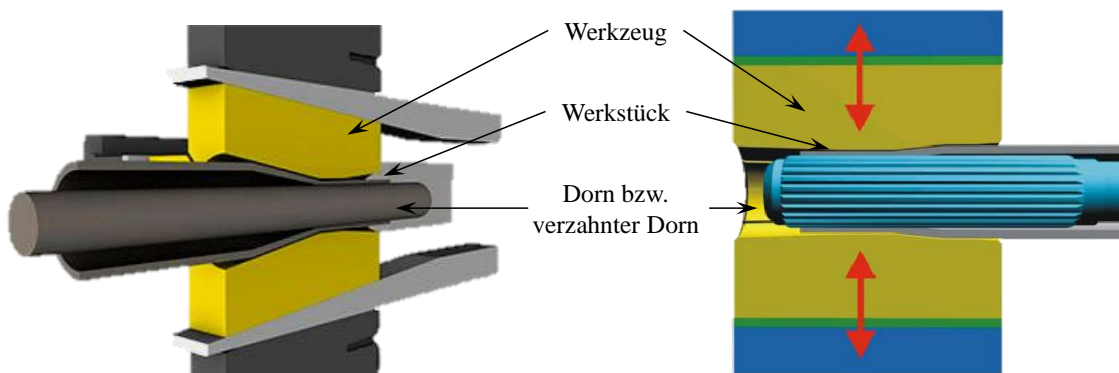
Anordnung der Werkzeuge um ein Werkstück herum und Wirkprinzip der Werkzeuge in einer Rundknetmaschine [Mül05, Gru12]
